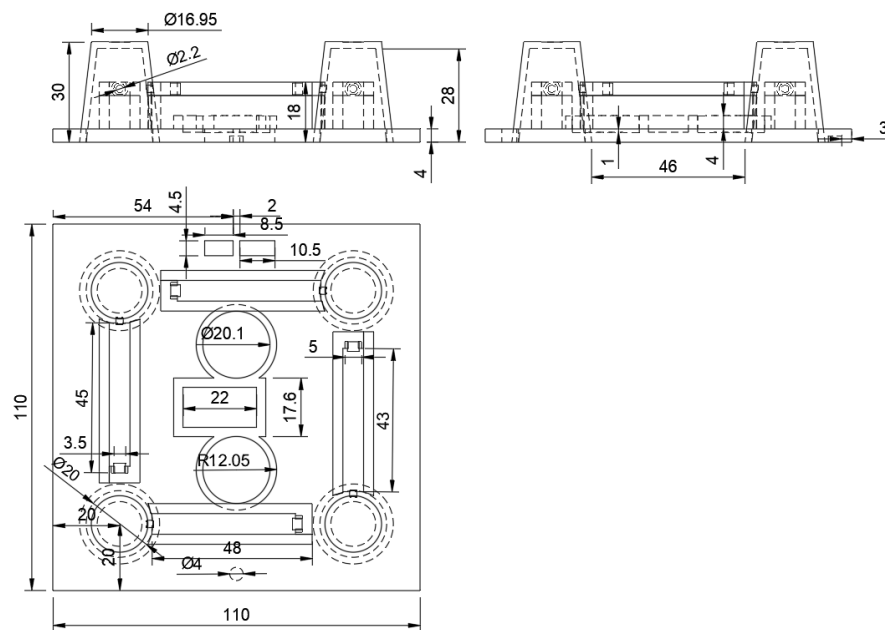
Ескіз корпусу пристрою для швидкої заміни інструмента маніпулятора
